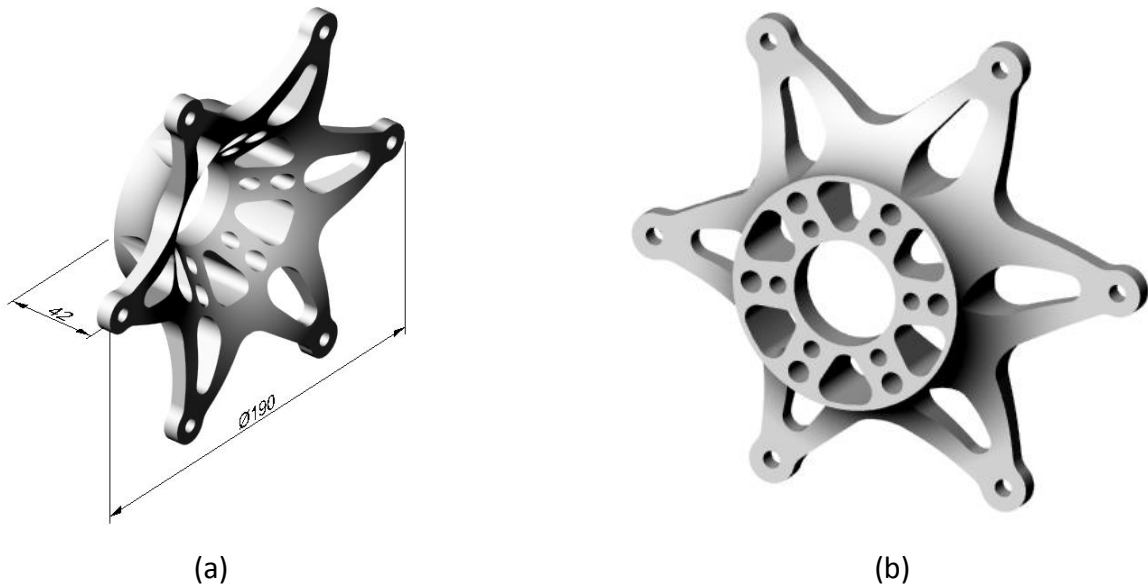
Flange traseira com dimensões gerais: (a) face externa, (b) face oposta.
